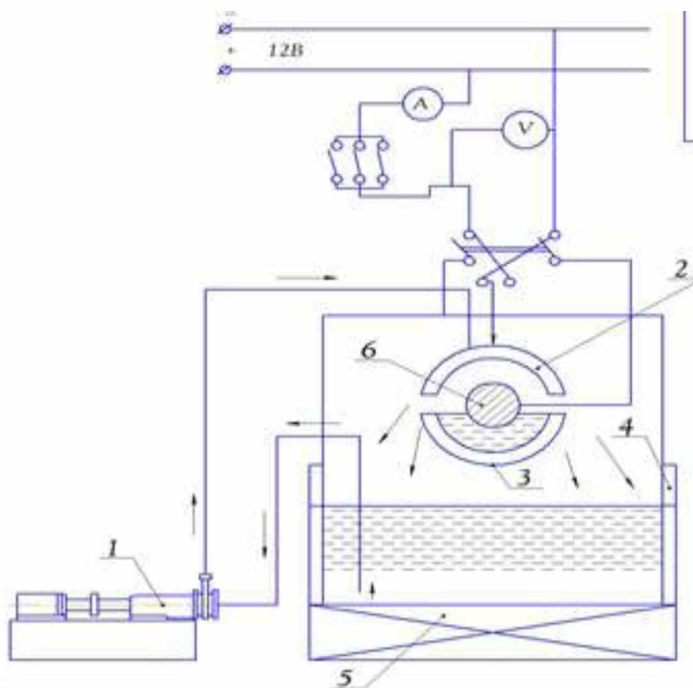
Схема установки для електролітичного покриття шийок валу
